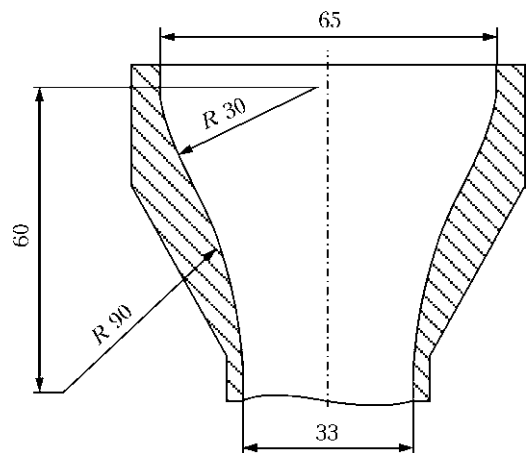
Схема защитного сопла для сварки в узкий зазор титана и сплавов на его основе
